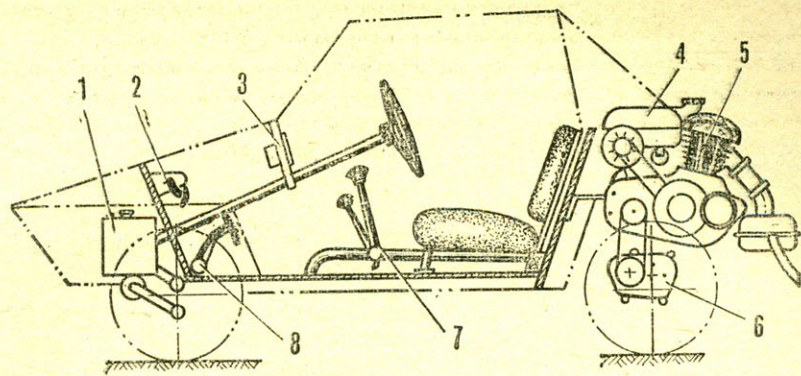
Основные узлы и агрегаты: 1 — аккумулятор, 2 — педаль газа, 3 — приборный щиток, 4 — топливный бак, 5 — двигатель, 6 — главная передача, 7 — рычаги переключения передач и реверса, 8 — педали тормоза и сцепления, 9 — главный тормозной цилиндр.
